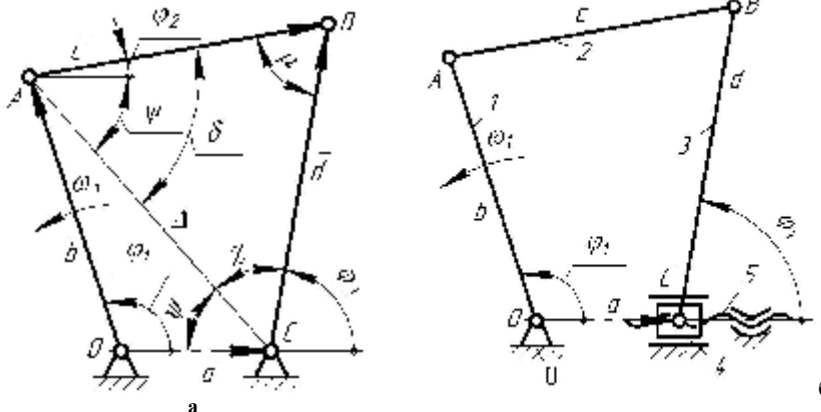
Двокривошипний шарнірний чотириланковий механізм:
